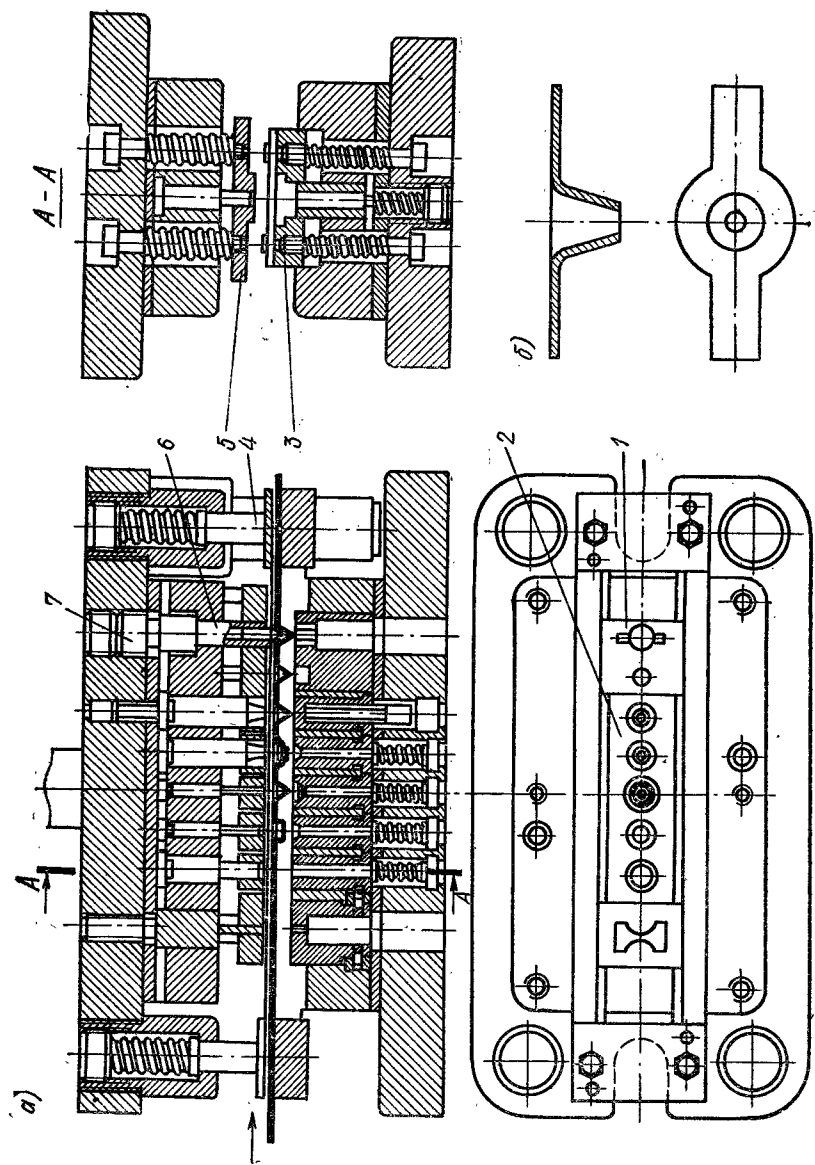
Многопозиционный (последовательный) штамп для вытяжки мелких деталей, работающий с автоматической подачей ленты
